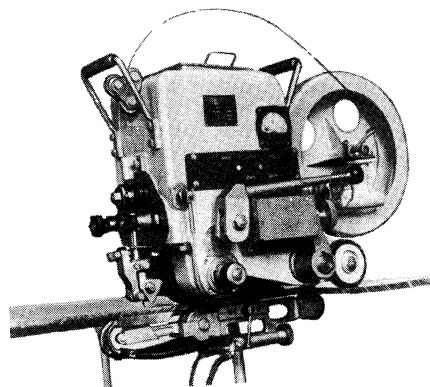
Трактор ТС-32 для дуговой сварки
